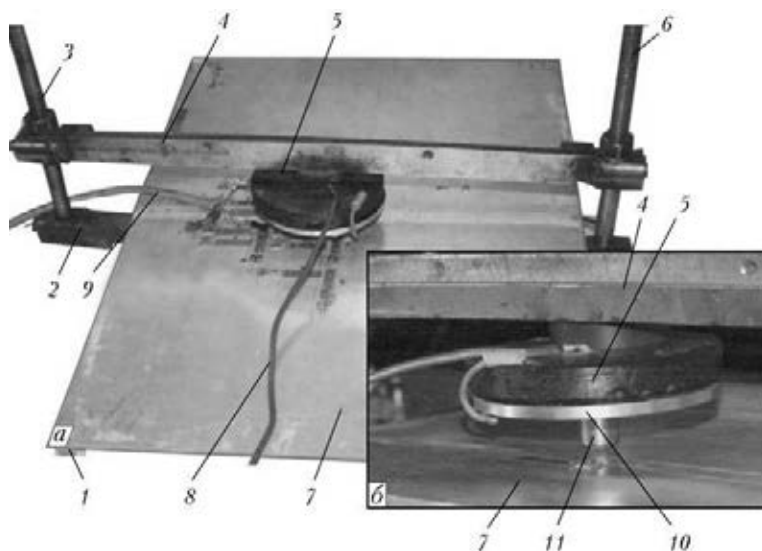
Внешний вид сборочного приспособления для ЭДО сварного соединения сплава АМг6 (а) и позиционирование индуктора на сварном шве (б) (1–11 — см. в тексте)
